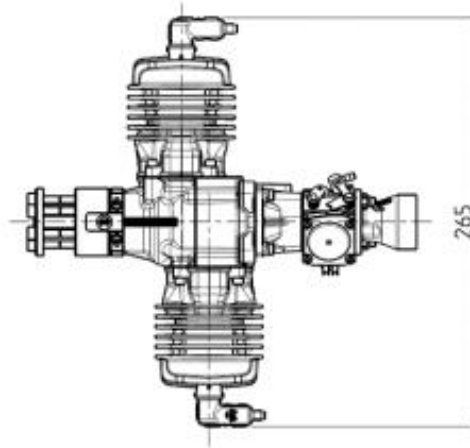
Vista planta 3W 56iB2 (Fuente: 3W modellmotoren)
